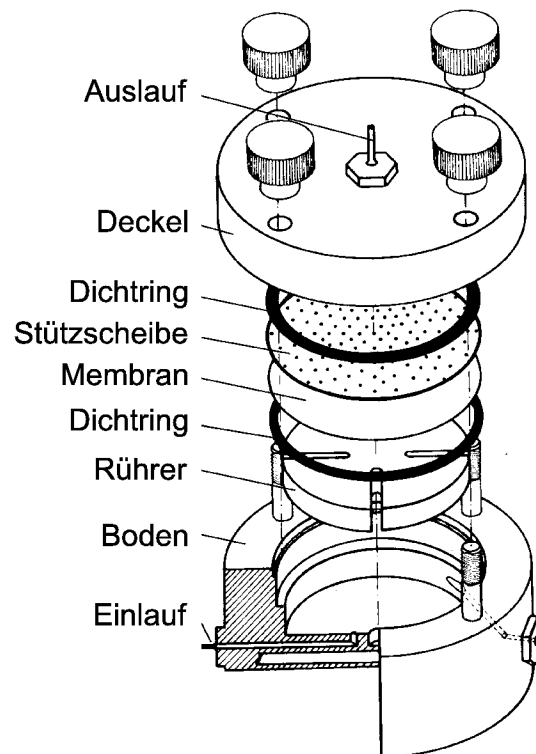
Explosionszeichnung des Membranreaktors.
